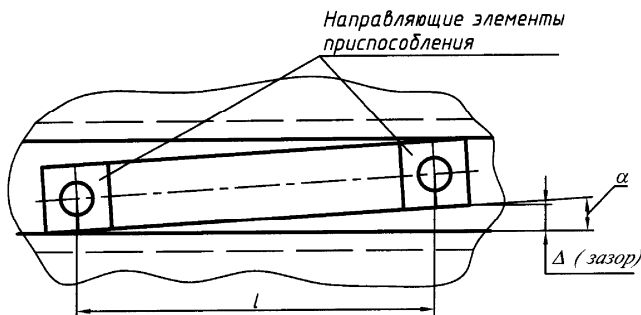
Формирование погрешности установки приспособления на стол станка
